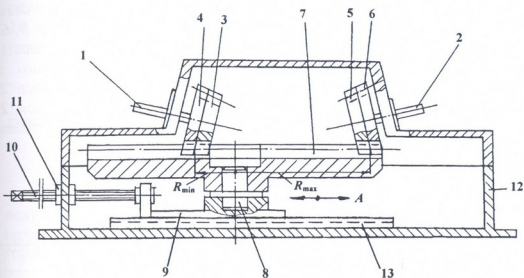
Двухступенчатый вариатор с коническими зубчатыми колесами
